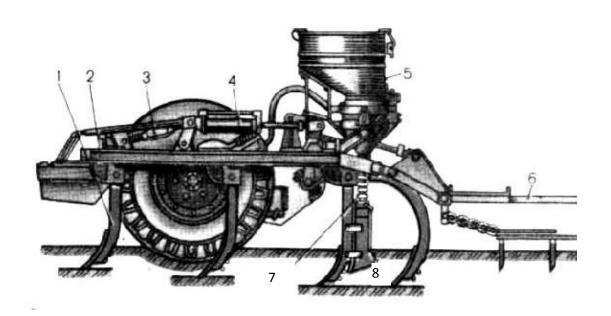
Чизель-культиватор (ЧКУ- 4+ Т4А (Т-150). Ширина захвата - 4 м. Глубина заделки 15...20 см. 1 — рыхлительная лапа, 2 — рама, 3 — регулятор глубины, 4 — гидроцилиндр, 5 — туковысевающий аппарат, 6 — навеска с бороной, 7 — лапа с тукопроводом для внесения удобрений, 8 — сошник.
